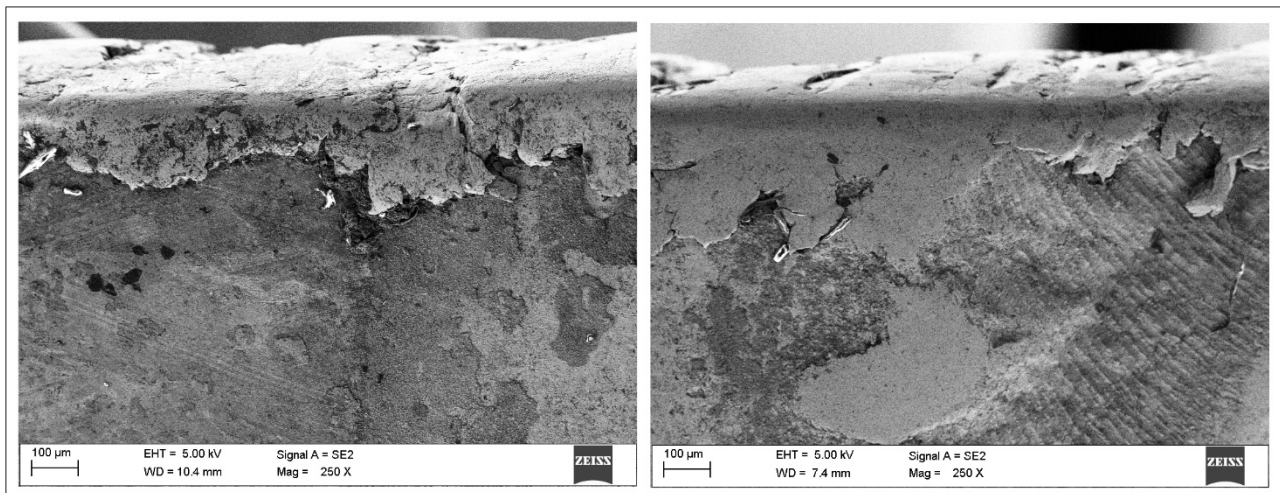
Acciaio AISI 347H Saldato . Ingrand. 250X in sezione planare
